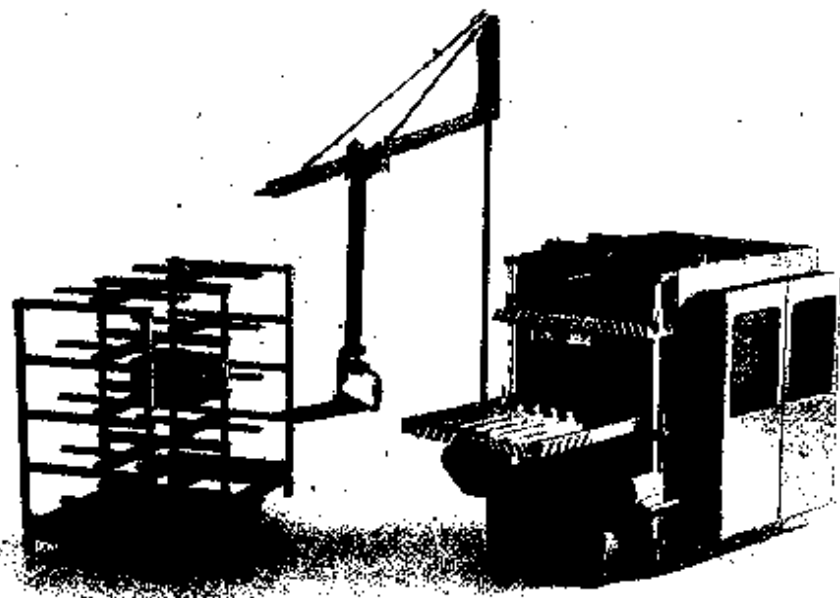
Формовочная установка СМТ-290 для изготовления стеновых бетонных камней
